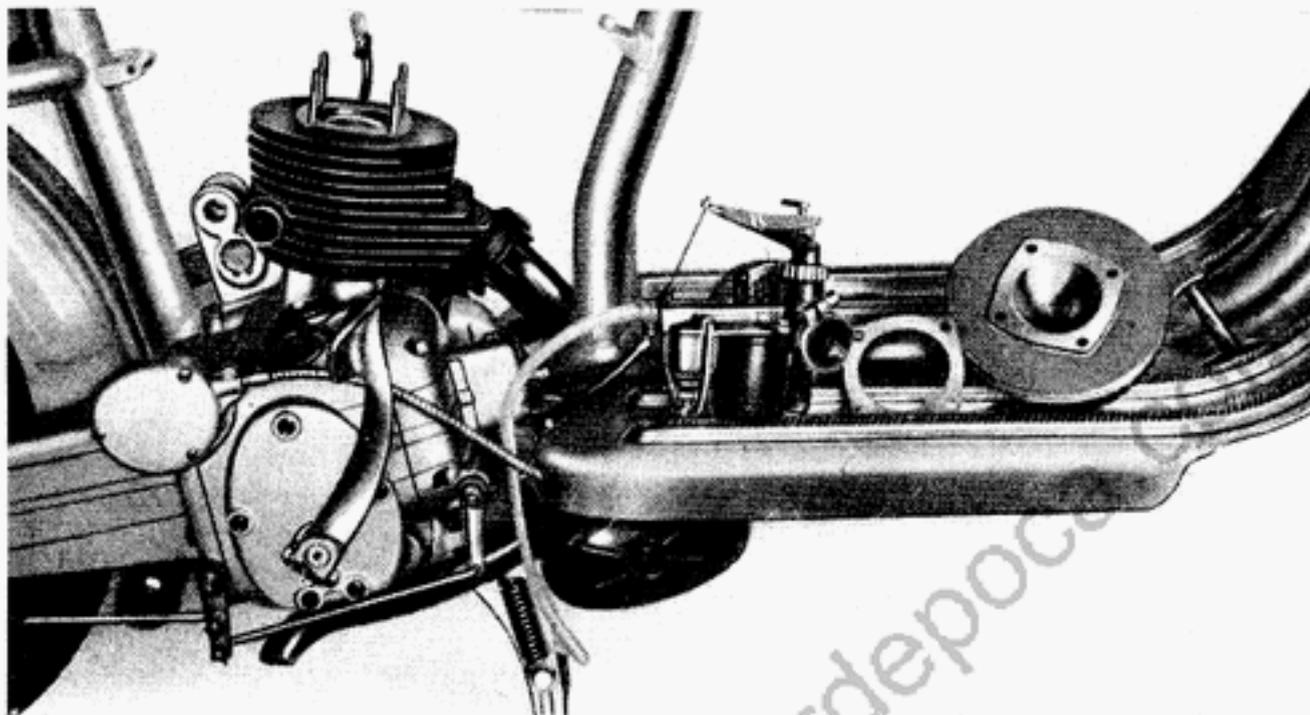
Smontaggio carburatore e cuffia, lato avviamento.
